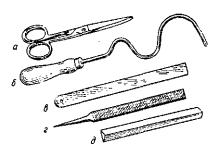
Режущий инструмент дпя стеклодувных работ. а — ножницы; б —крючок; в — нож: г- напильник; д — призма.
